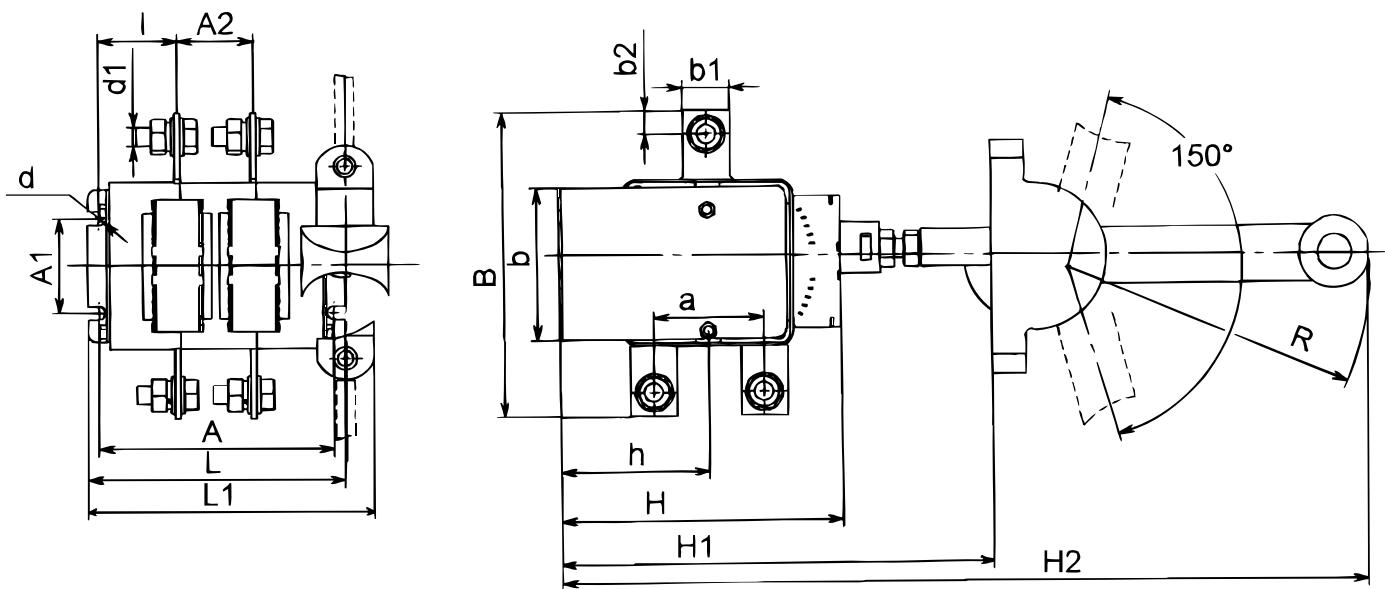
Выключатель-разъединитель на два направления двухполюсный с передней смещенной рукояткой
